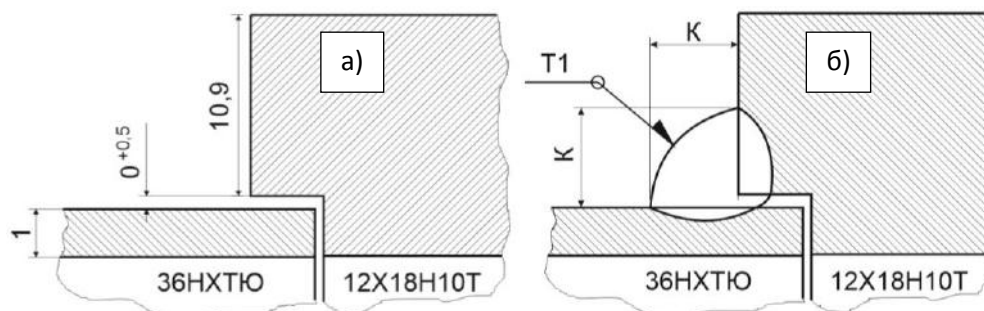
а) схема сборки; б) схема сварки.
